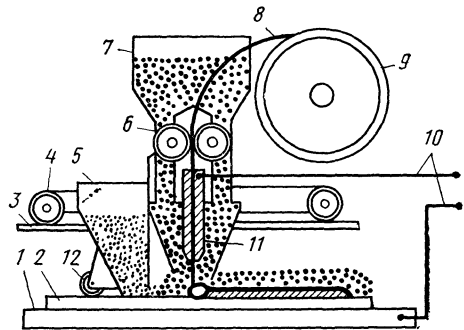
Схема автоматической наплавки порошкообразными наплавочными материалами под флюсом на установке НД-Ш-1
